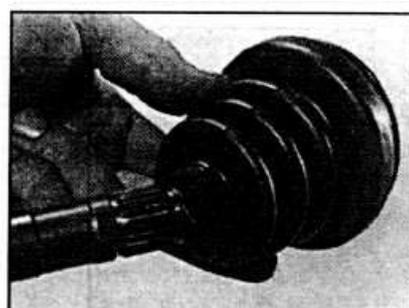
Установка нового защитного чехла на приводной вал.
